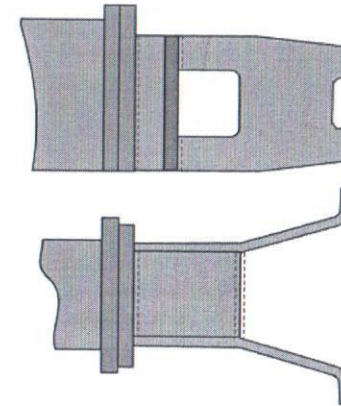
Контроль околошовных зон сварного соединения частей тормозного блока
